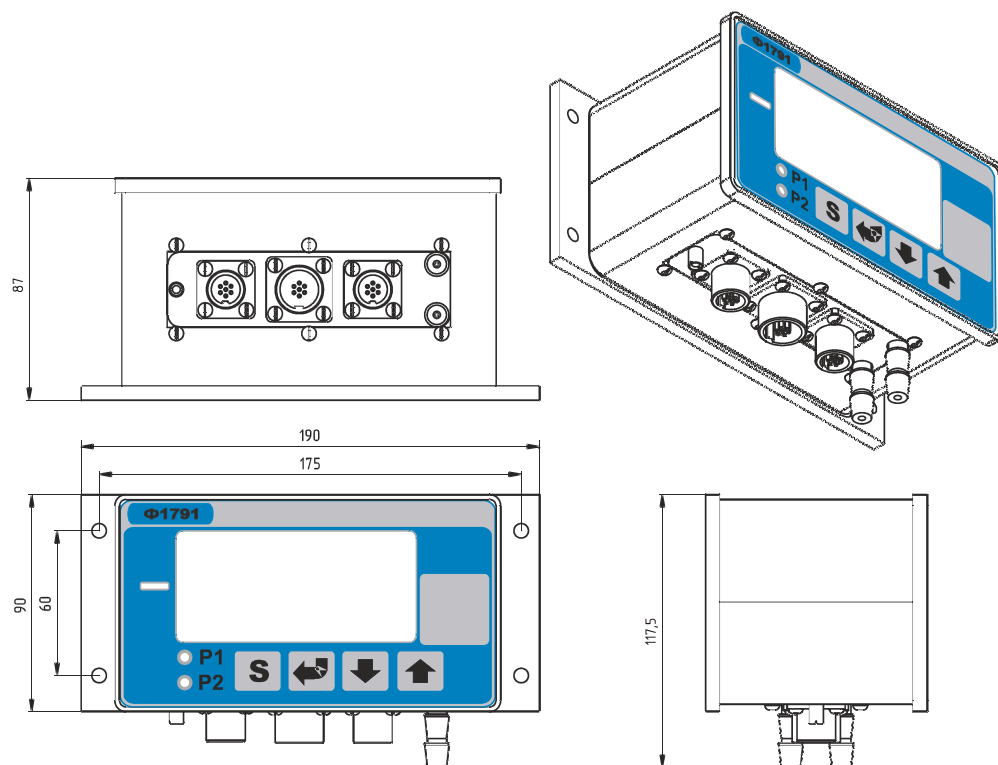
Внешний вид и габаритные размеры Φ1791.2
